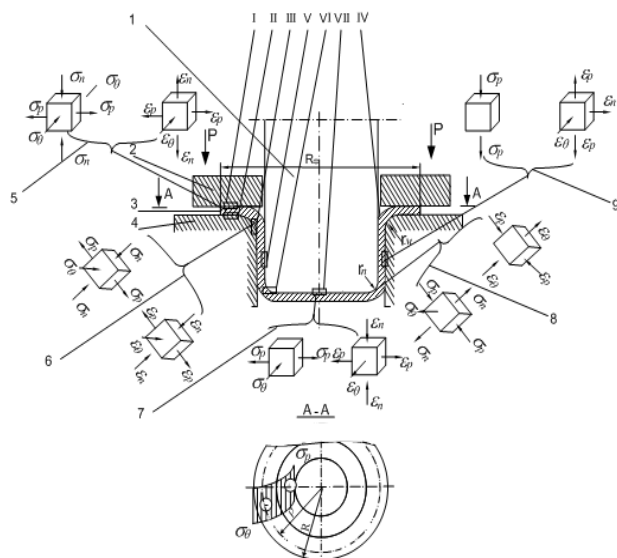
Схема глубокой вытяжки осесимметричных заготовок из листовых сталей: 1 – пуансон; 2 – прижим; 3 – заготовка; 4 – матрица; 5-9 – напряжения, деформации в элементах заготовки, I-VII – трибосистемы
